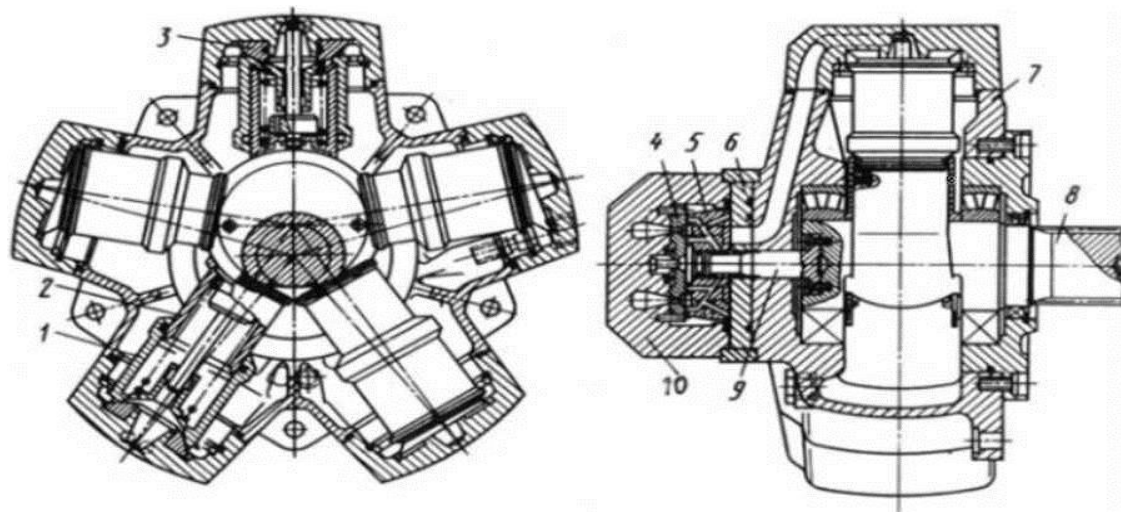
Гидромотор типа МР с качающимися цилиндрами
